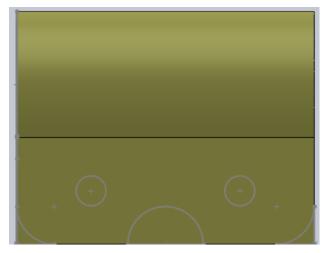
Diseño de la Horquilla Fuente. Autores
